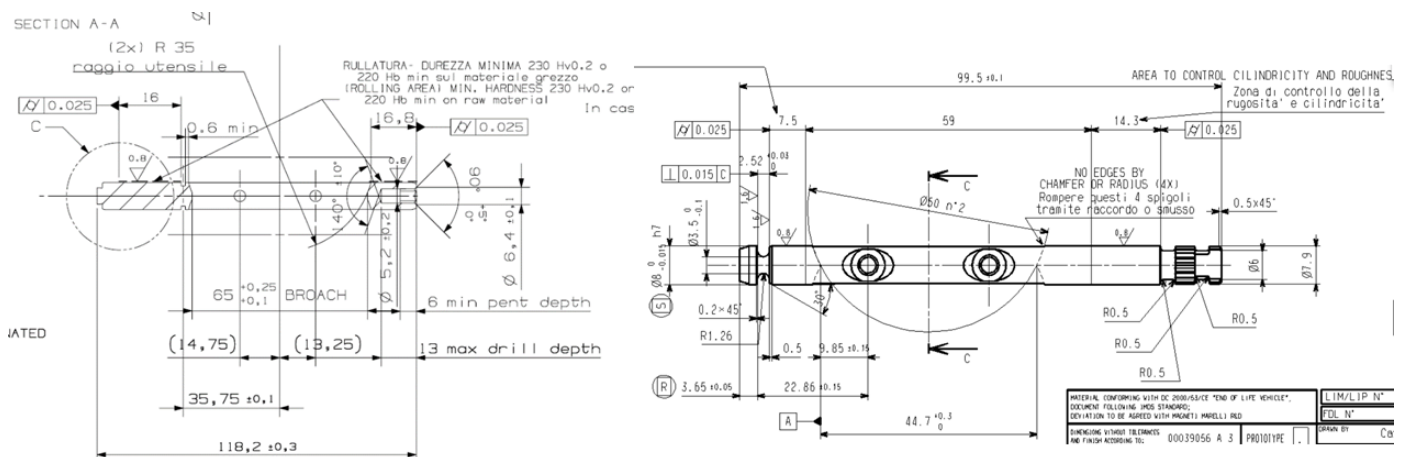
Desenhos esquemáticos do eixo usado (dimensões em mm)
